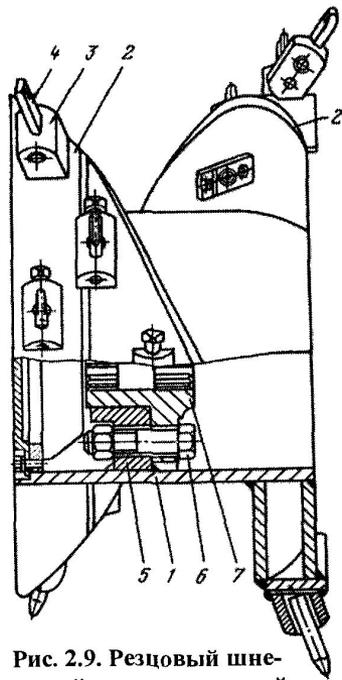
Резцовый шнековый исполнительный орган очистного комбайна:
